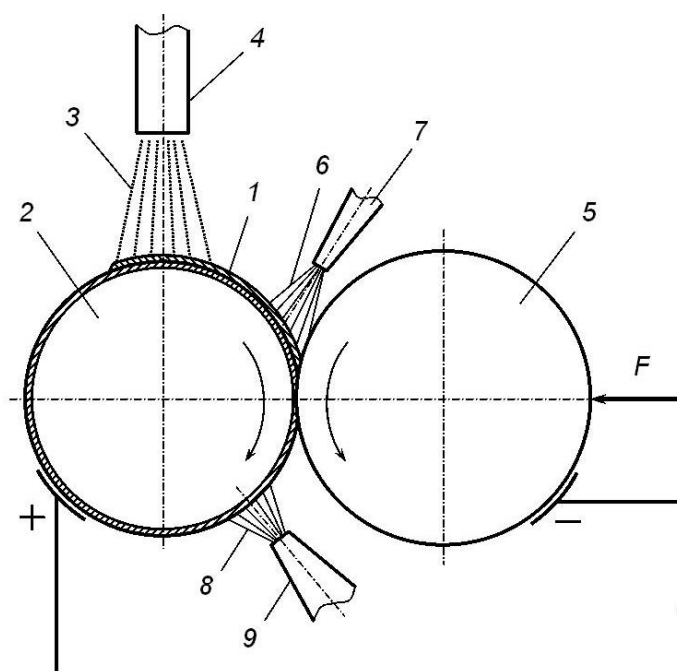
Схема комбинированного нанесения покрытия: 1 – покрытие; 2 – деталь; 3 – плазменная струя; 4 – плазматрон; 5 – ролик; 6, 8 – охлаждающая струя; 7, 9 – форсунки; F – сила прижима ролика
